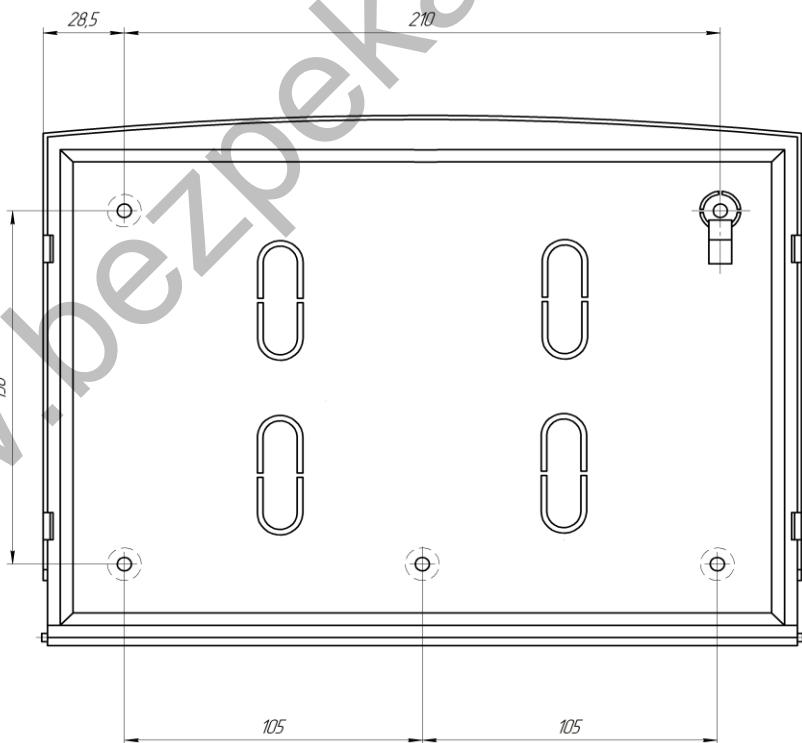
Розташування отворів для кріплення на корпусі АПК
